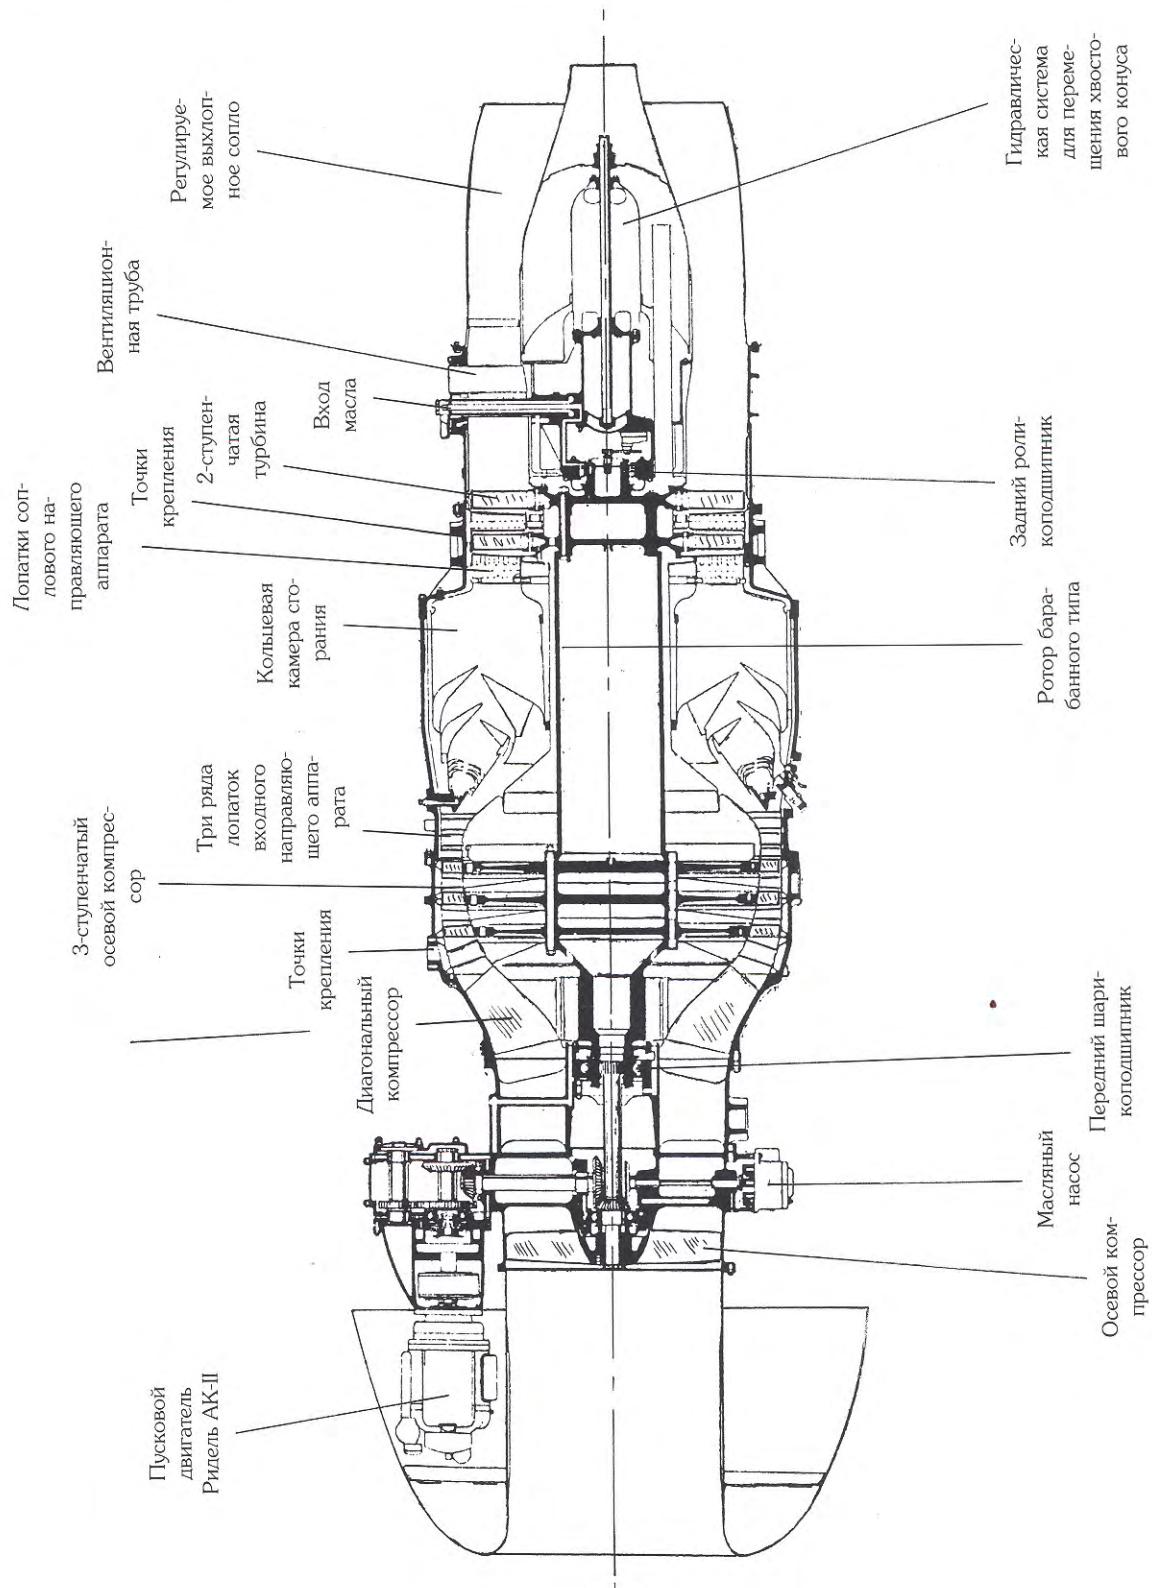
Турбореактивный двигатель Хейнкель-Хирт 109-011 А-0
